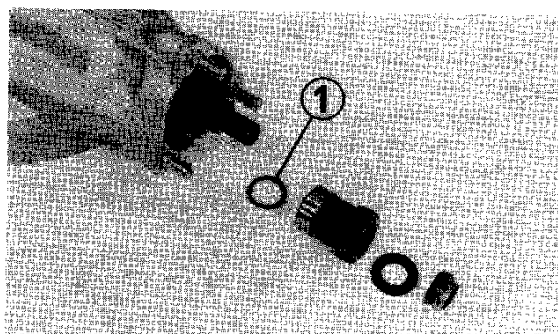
(1) O-Ring 20,8 x 2,4
